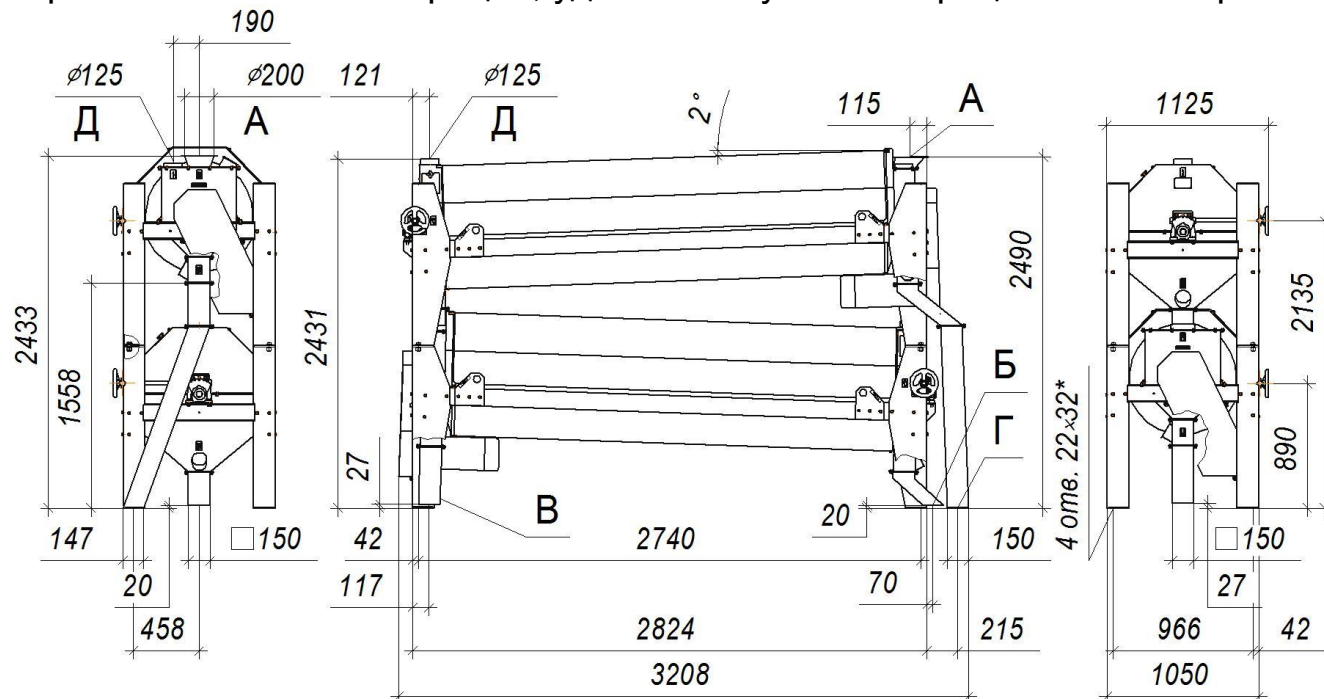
Установочные и присоединительные размеры блоков триерных БТМ-800-8Б и БТМ-800-8Е:
